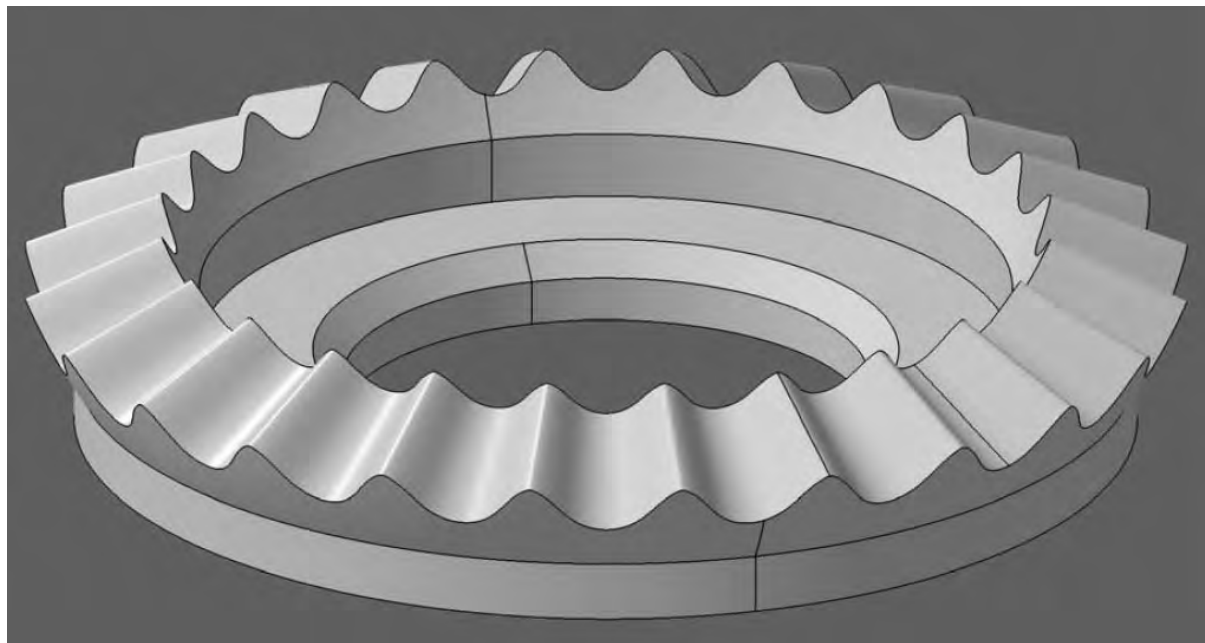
Зубчатая поверхность сателлитного колеса, образованная на наружной конической поверхности
